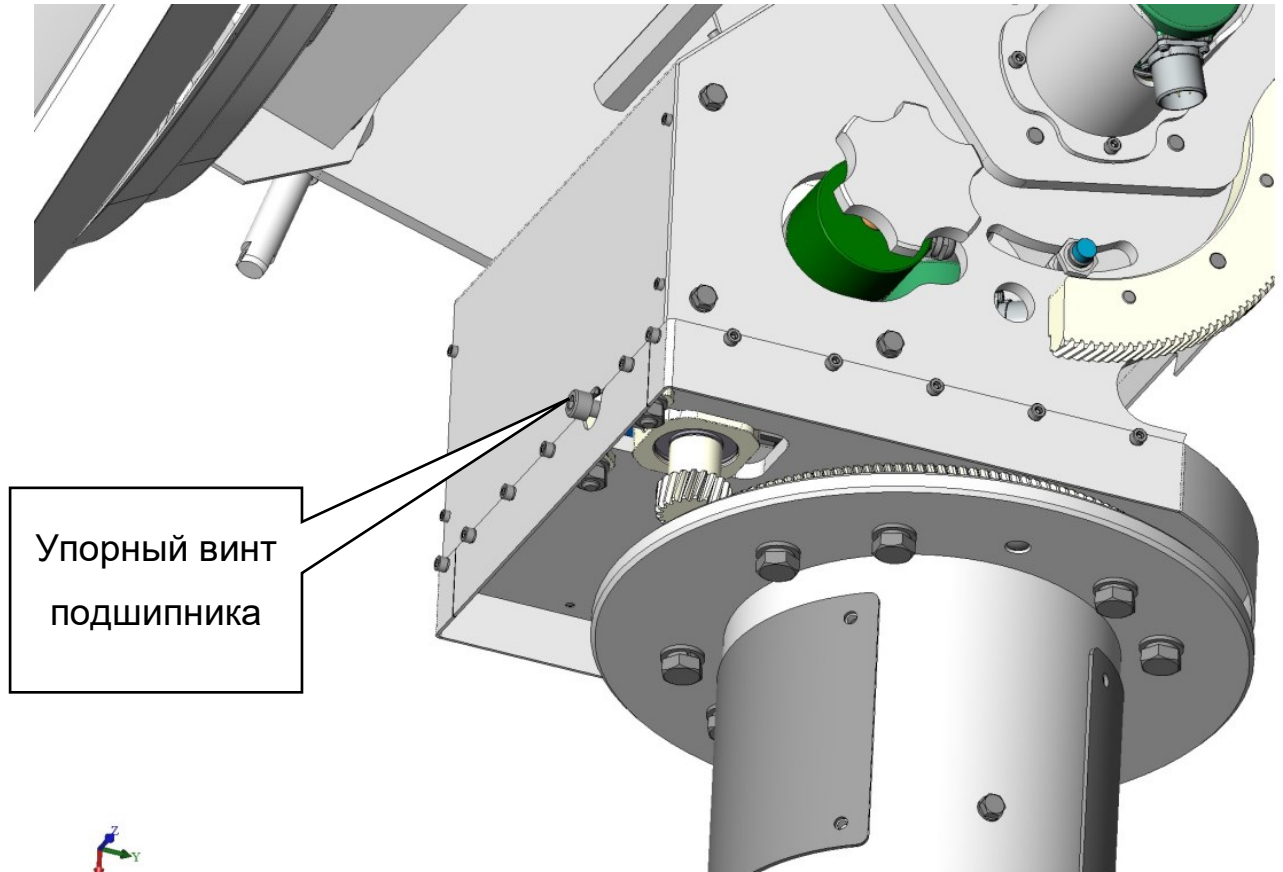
Позиция упорного винта подшипника по азимуту
